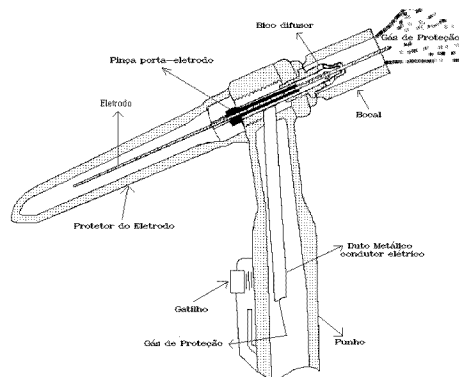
Porta eletrodo (“tocha”) para a soldagem TIG.
